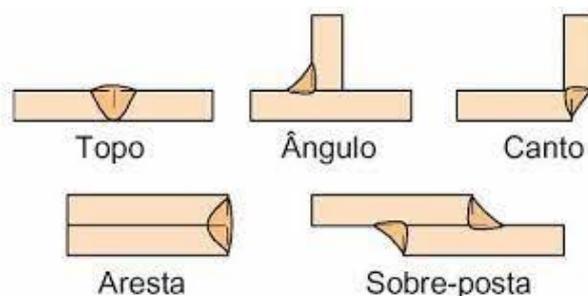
Tipos de junta na soldagem eletrodo revestido
